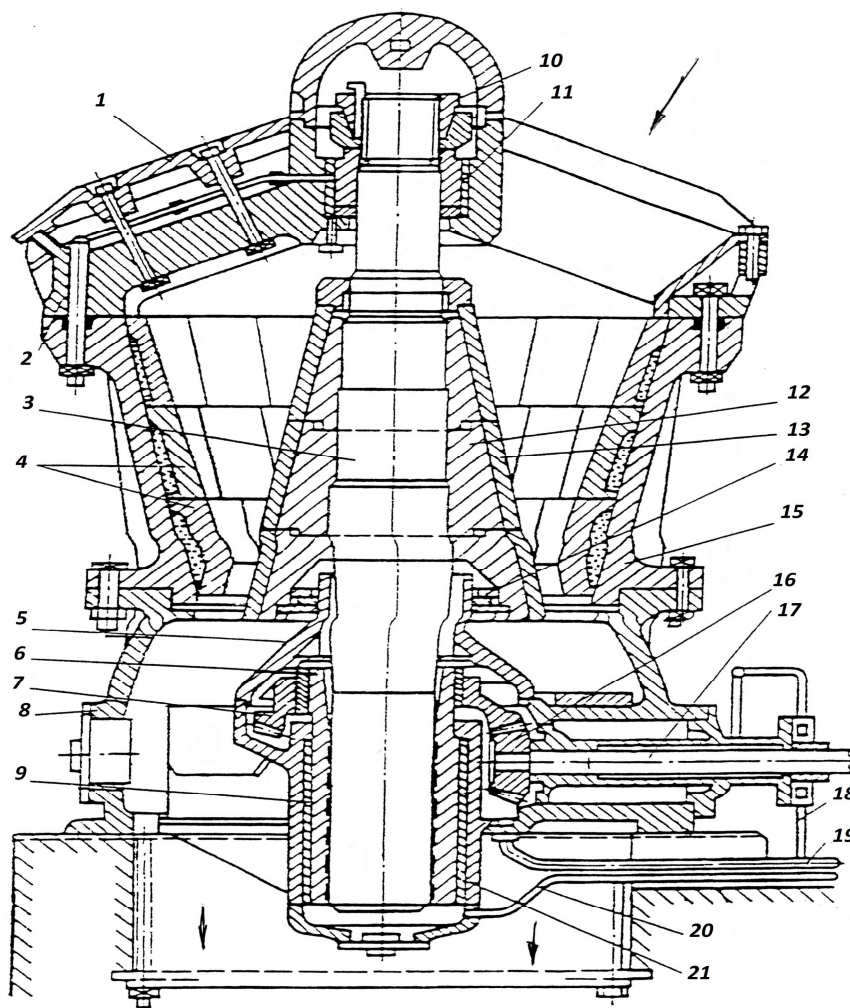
Конусная дробилка крупного дробления (стрелками показаны направления загрузки и выгрузки материала): 1 - плита сменная; 2 - крышка; 3 - вал; 4 - футеровка чаши; 5 - втулка; 6 - эксцентрик; 7 - колесо коническое; 8 - основание; 9 - втулка бронзовая; 10 - гайка; 11 - опора сферическая; 12 - конус дробящий; 13 - футеровка конуса (бронеконуса); 14 - уплотнение; 15 - чаша; 16 - шестерня коническая; 17 - вал приводной; 18, 19, 20 - маслопроводы; 21 - стакан опорный
